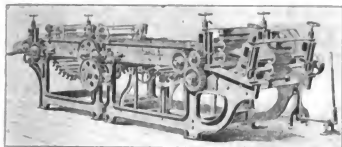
Hechelmaschine (breaker) der Watson Machine Comp.
